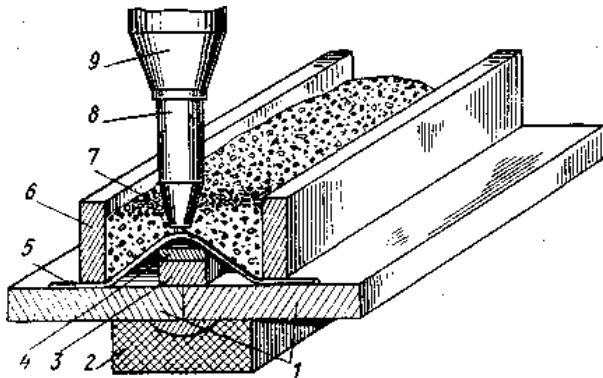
Схема автоматичного зварювання міді вугільним електродом під шаром флюсу: 1 – деталі, що зварюються; 2 – графітова підкладка; 3 – присадний метал; 4 – латунна смуга; 5 – мідні дроти; 6 – захисні планки; 7 – флюс; 8 – вугільний електрод; 9 – зажимний та струмопровідний пристрій автоматичної головки
